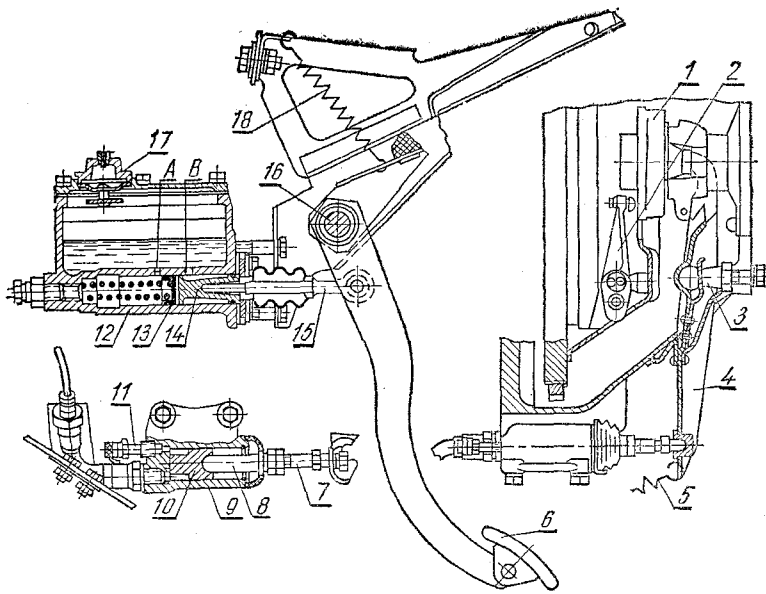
Гидравлический привод муфты сцепления автомобиля ГАЗ-21 «Волга»:
